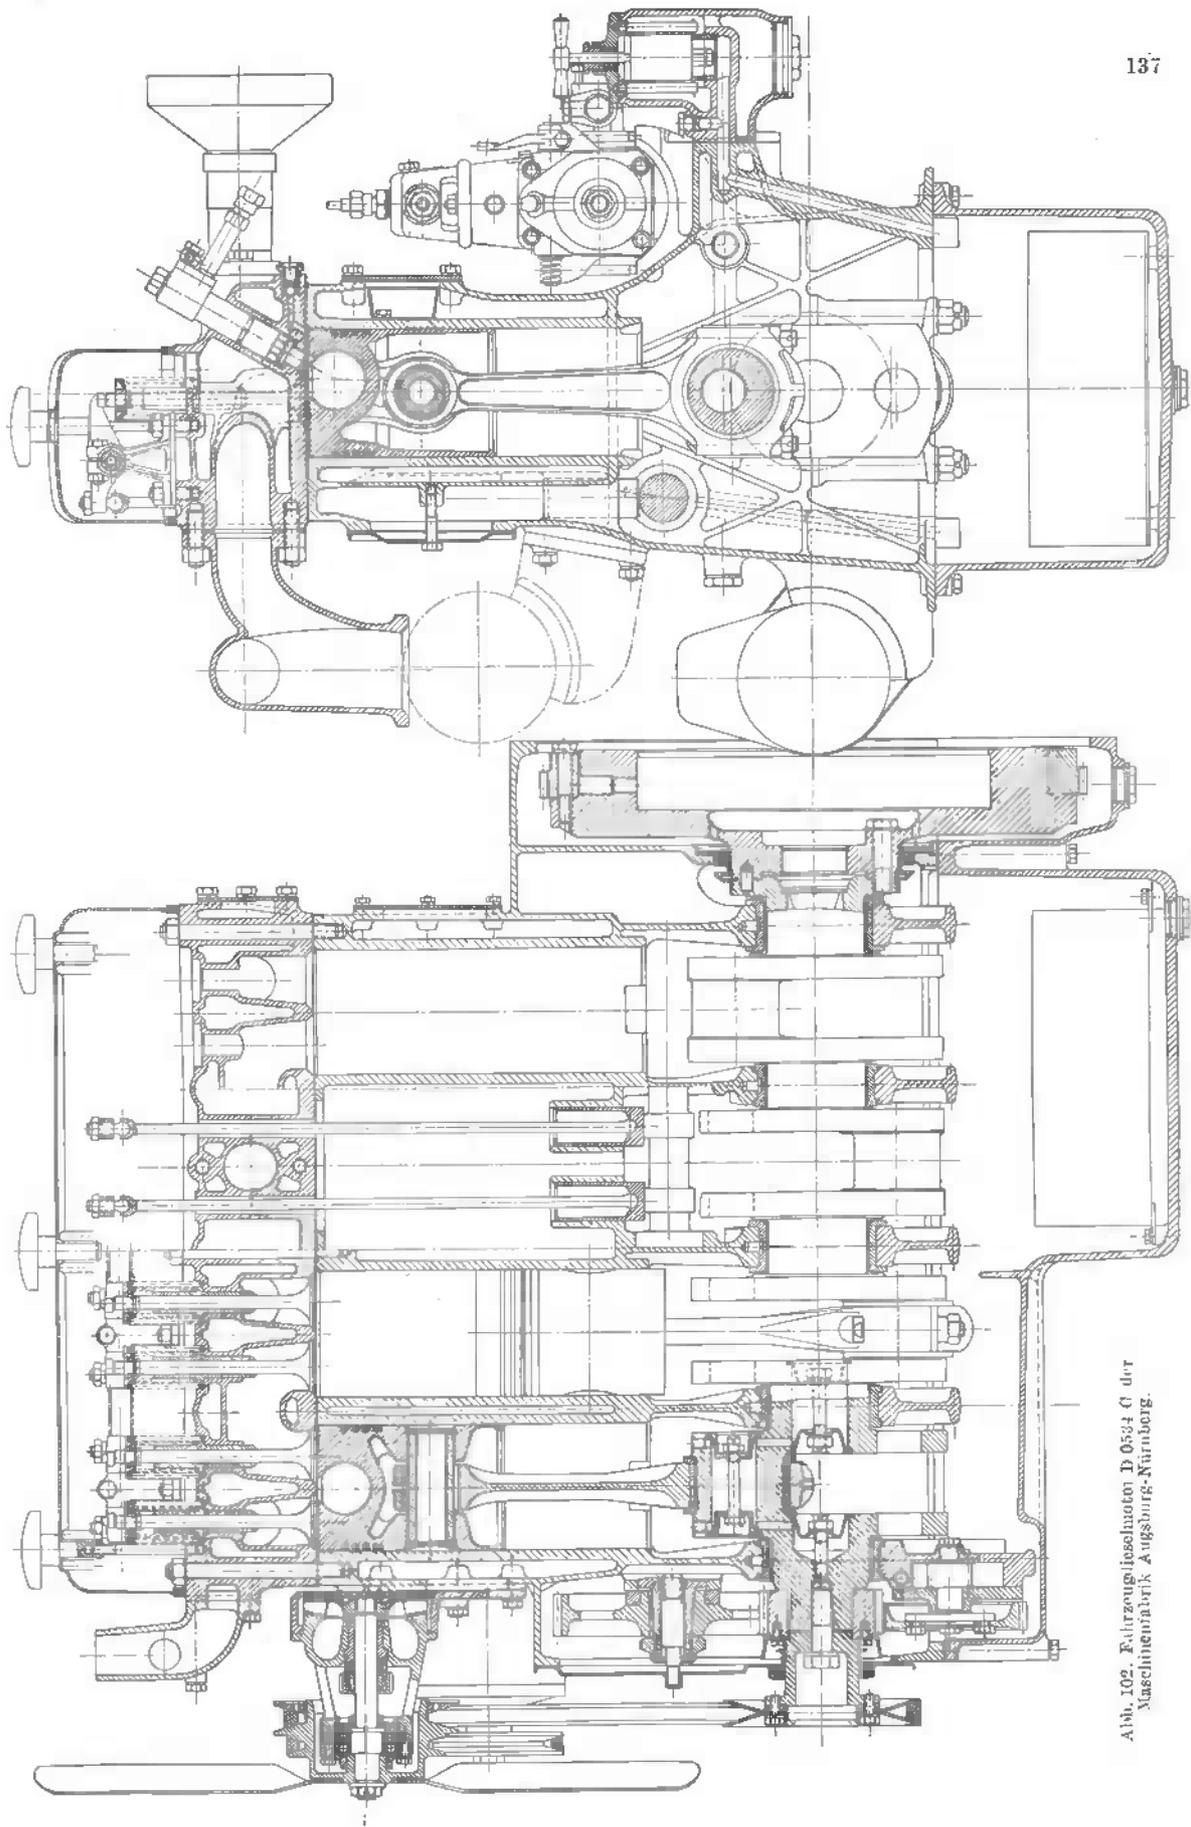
Fahrzeug Dieselmotor D 0534 G der
